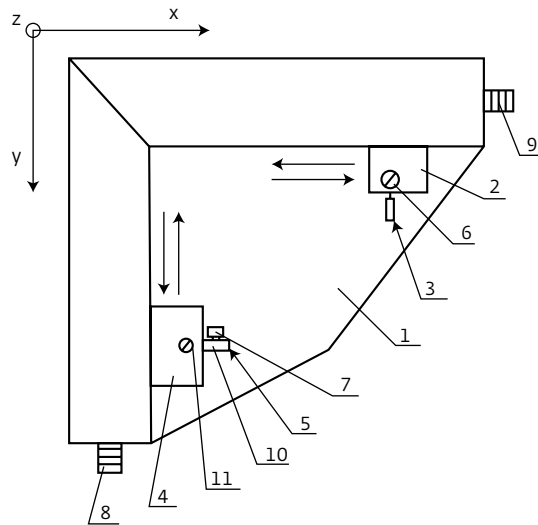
Устройство для изготовления зондов на основе кварцевых резонаторов: 1 – платформа; 2 – первый держатель; 3 – кварцевый резонатор; 4 – второй держатель; 5 – игла; 8 – первый винт; 9 – второй винт
